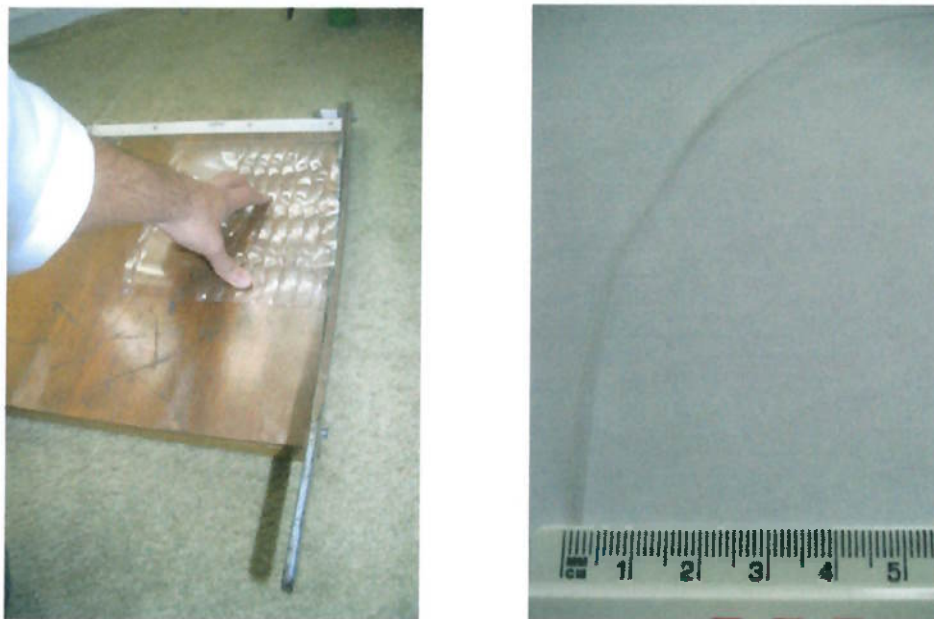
e 2.4 – Detalhe do corte das imperfeições
